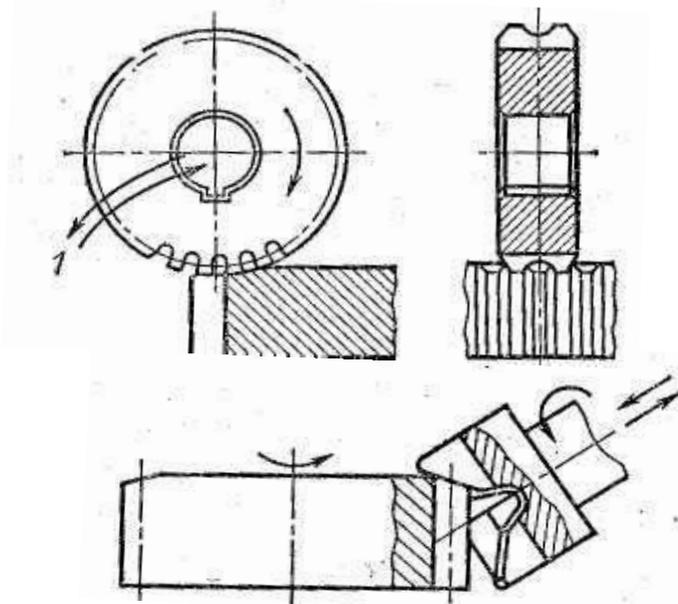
Закругление зубьев дисковой и конусной фрезой
